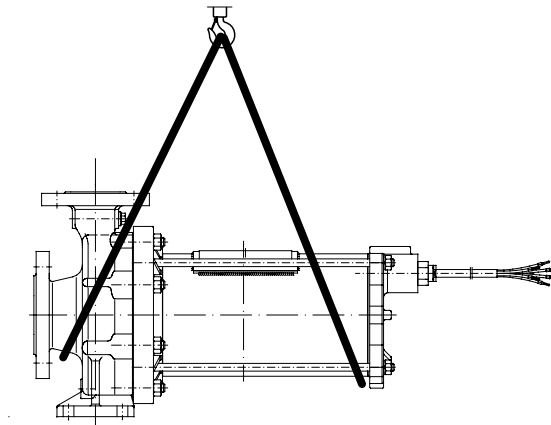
Hebezeug befestigen an Pumpenaggregat
